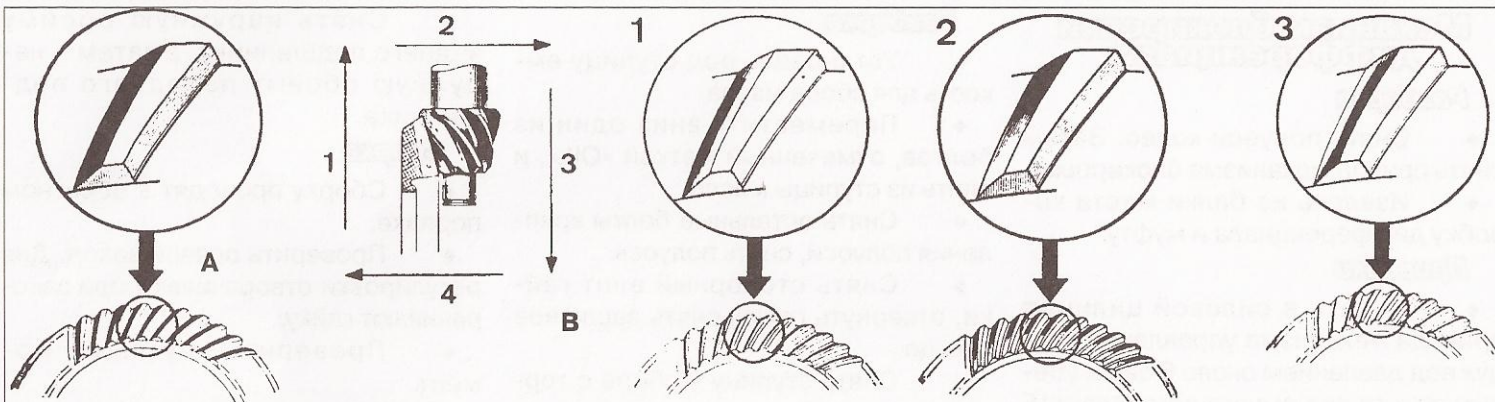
Обозначения для регулировки опорной поверхности зубьев конической пары шестерен.
